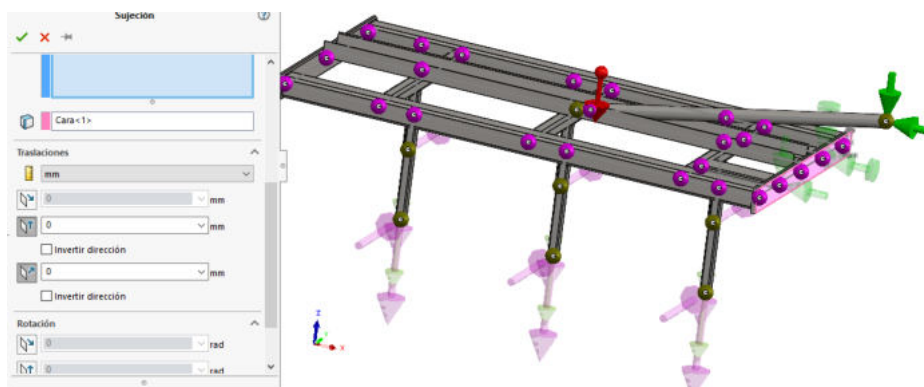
Condiciones de apoyo sobre la barra circular de la estructura.
